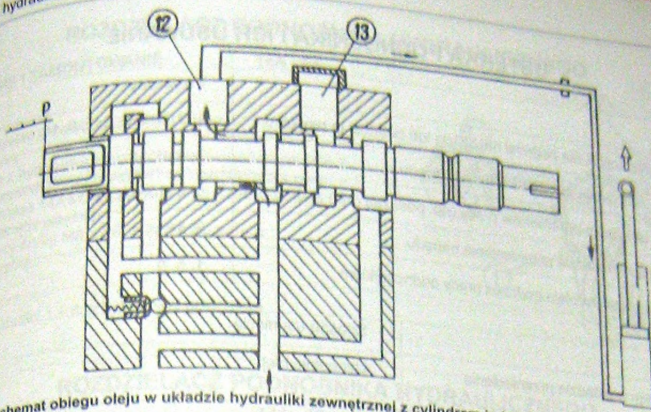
A - 11. Schemat obiegu oleju w układzie hydrauliki zewnętrznej z cylindrem dwustronnego działania.
